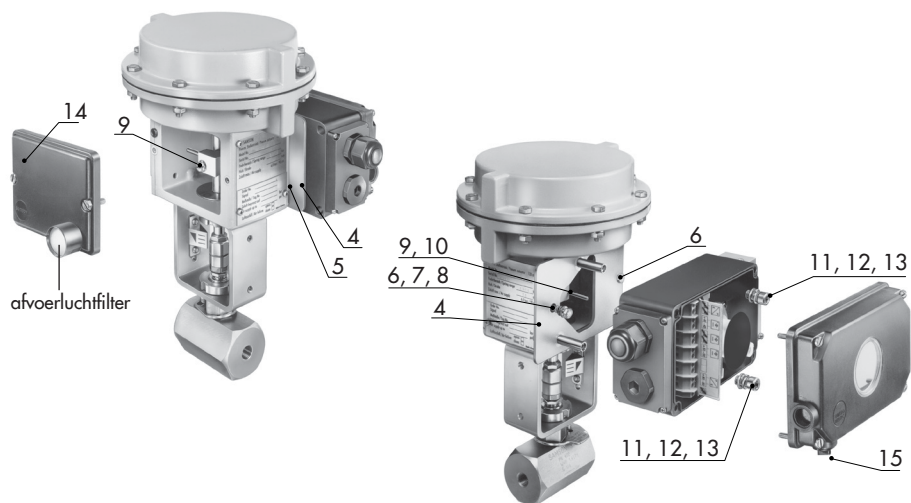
Montage aan SAMSON-slaaandrijving type 3277-5 · externe instrumentenluchttoevoer
